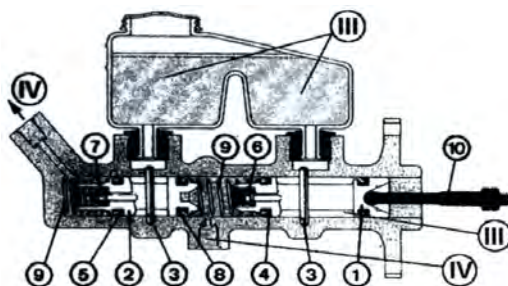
Положение деталей главного цилиндра с центральными поршневыми клапанами при торможении
